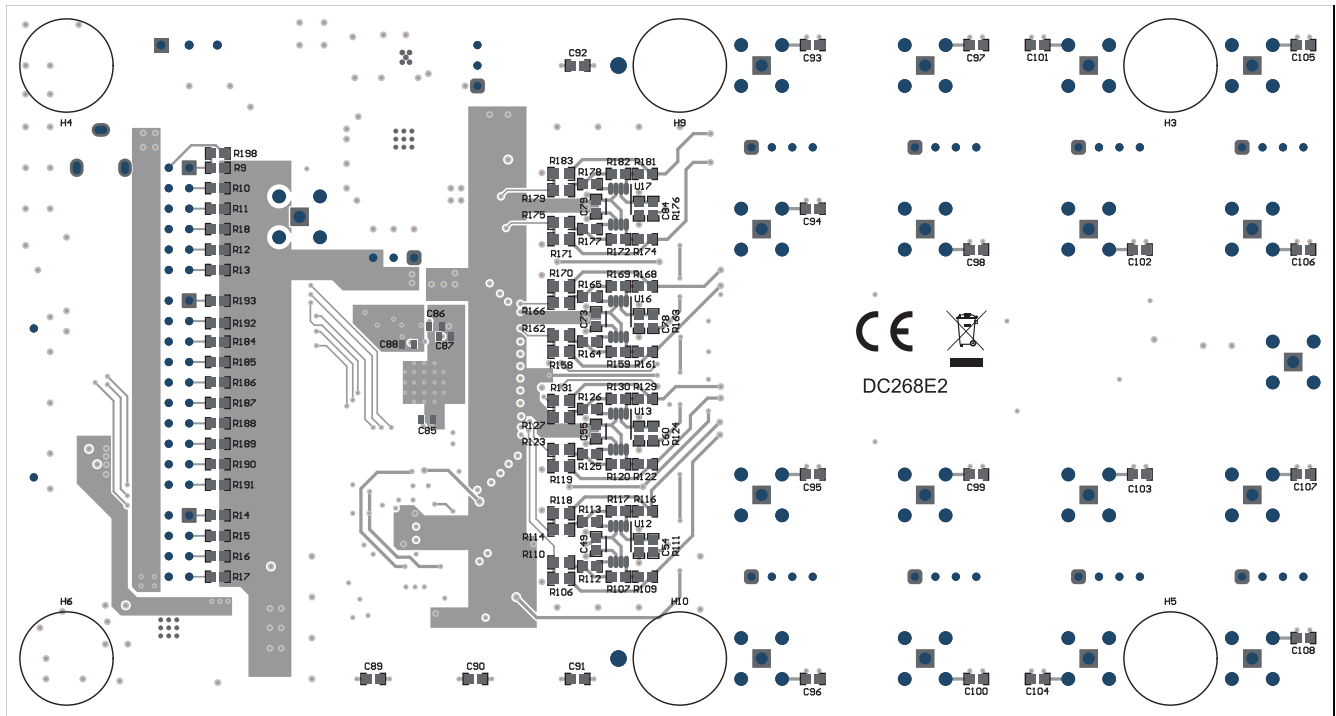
ADS127L18EVM 的 PCB 布局 (底视图)
